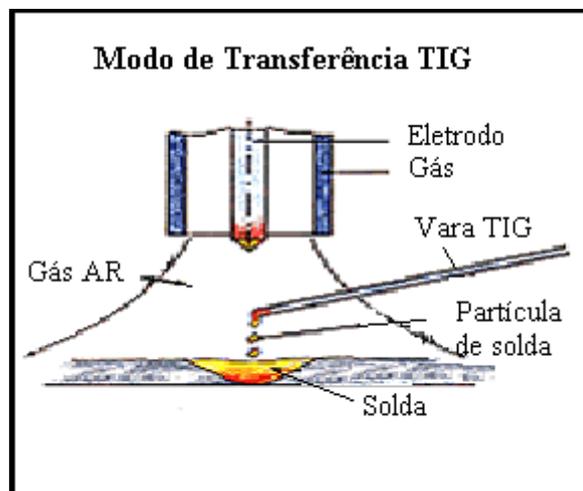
Processo de soldagem *Tungsten Inert Gas* (TIG).
